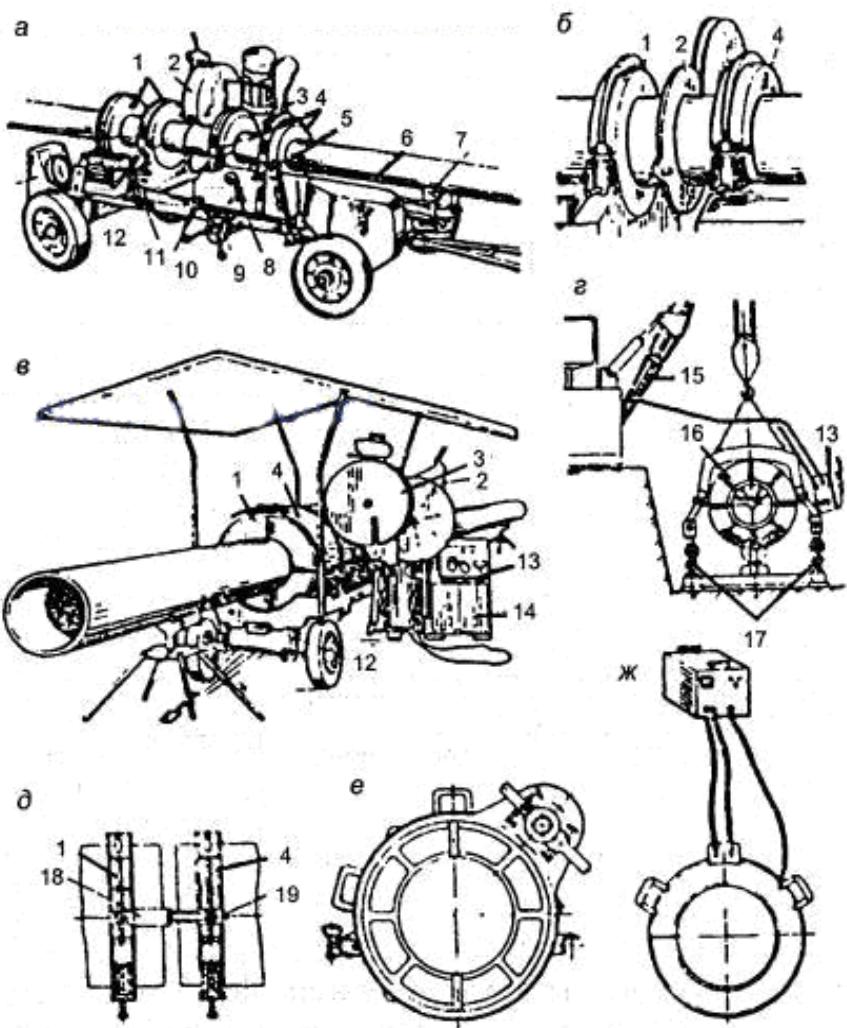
Установки и оборудование для сварки пластмассовых (полиэтиленовых) труб:
